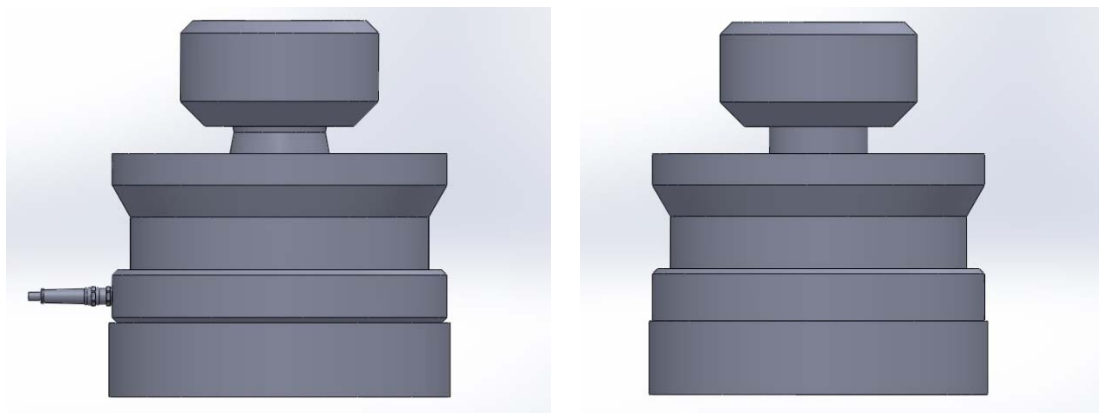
CAD del fabricante (izquierda) y Trd V1, Caso 0, una versión adaptada eliminando pequeñas geometrías (derecha)
